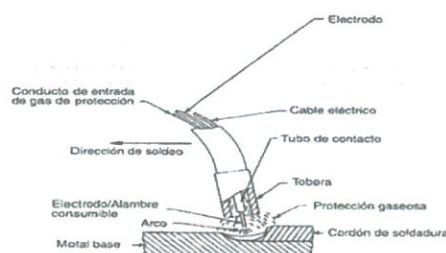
Soldadura por arco de metal y gas
